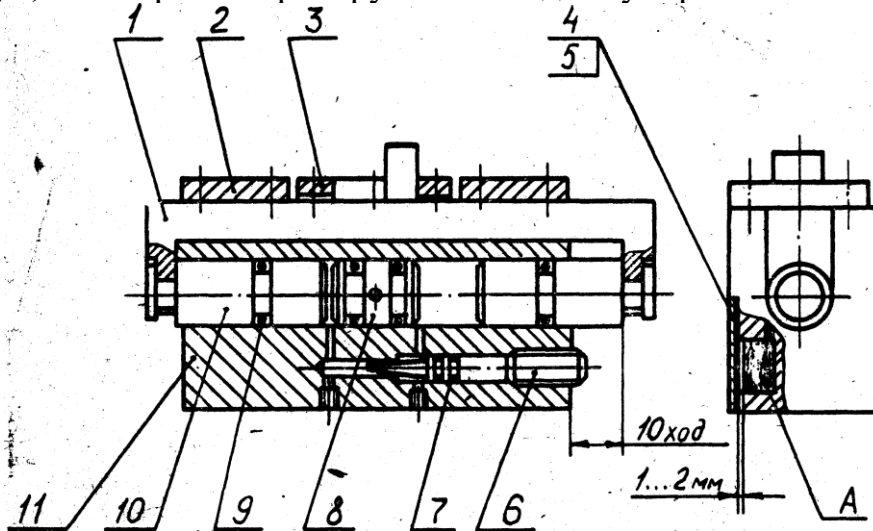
Амортизатор повороту: 1 – скоба; 2 – пластина; 3 – накладка; 4 – кришка; 5 – прокладка; 6 – голка; 7 – кільце гумове; 8 – пробка; 9 – кільце гумове; 10 – шток; 11 – корпус.
